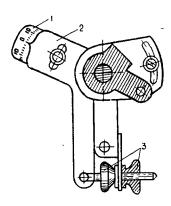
Октан-корректор: 1 и 2 — нижияя и верхняя пластины; 3 — регулнровочные гайки.
